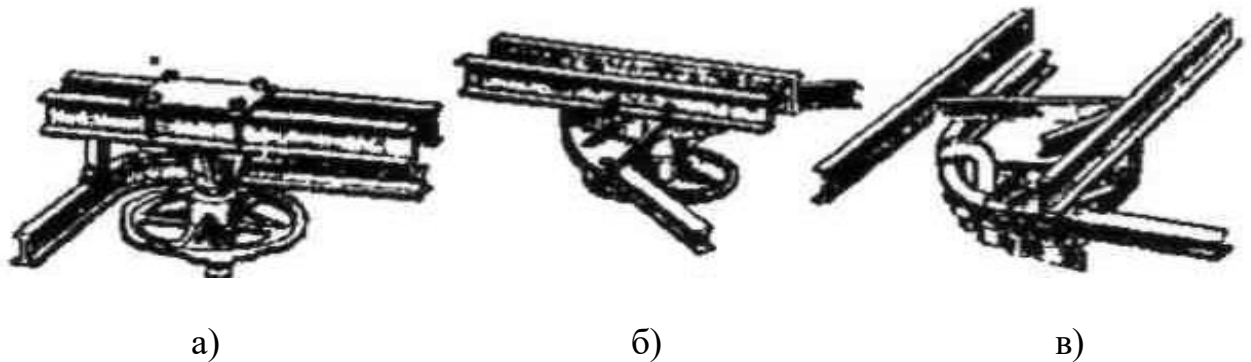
Поворотний пристрій: а) із зірочкою; б) із блоком; в) з роликовою батареєю
